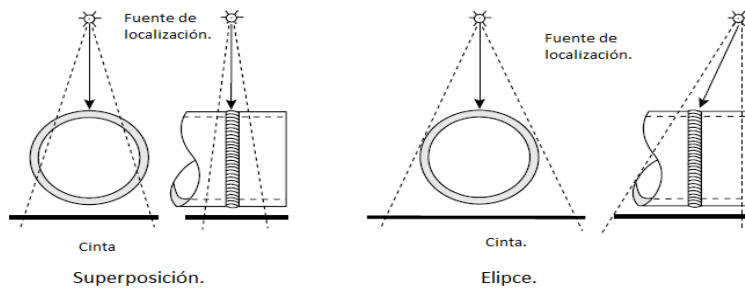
La exposición de doble pared, la técnica de doble vista.
